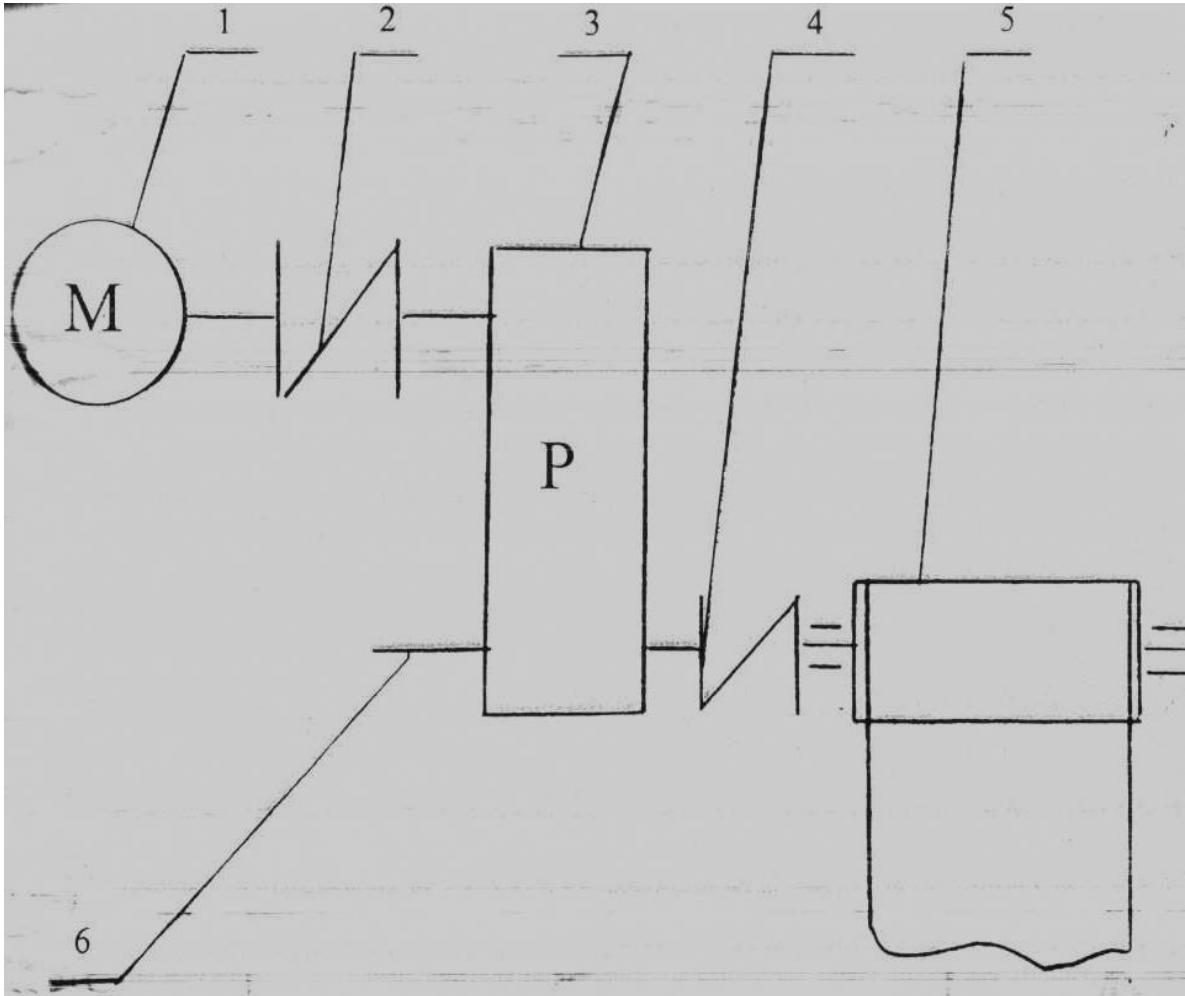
Схема приводу стрічкового конвеєра: 1 – електродвигун; 2, 4 – муфти; 3 – редуктор; 5 – привідний барабан з опорами; 6 – вихід вала редуктора на привід
